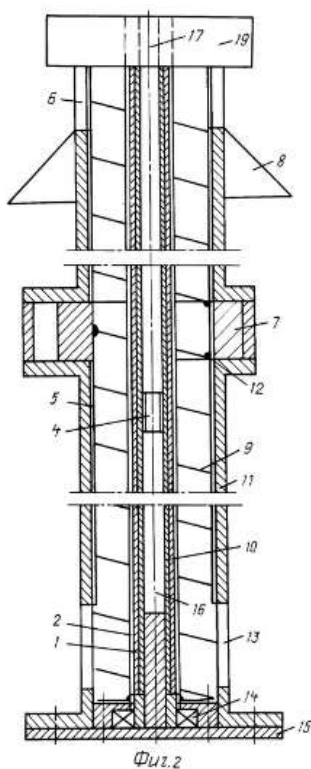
Шнековый транспортер с расположением редуктора в середине транспортера
